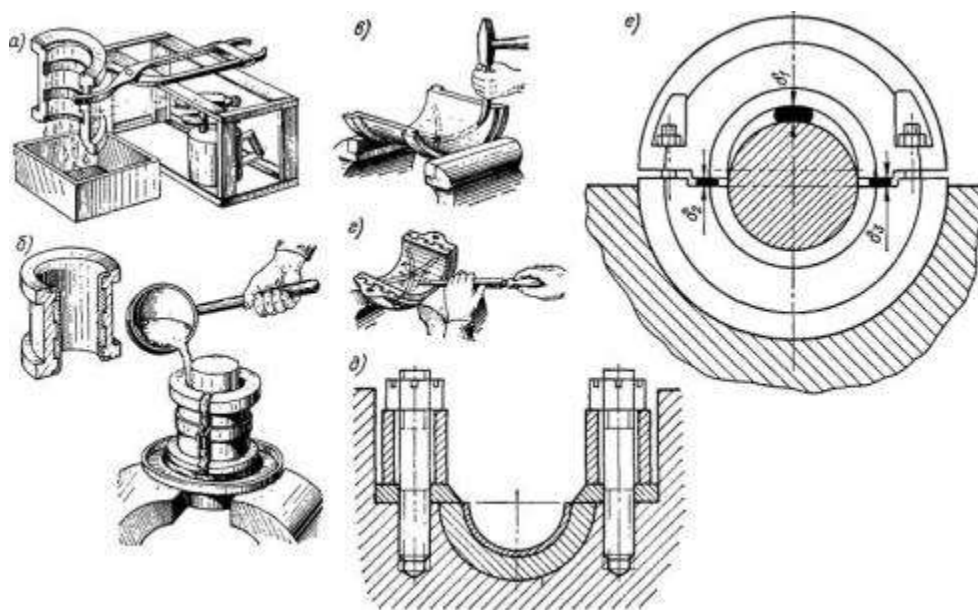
Ремонт разъемного подшипника скольжения: а — выплавка баббита; б -заливка баббита; в -вырубка смазочных канавок; г -шабрение; д — сборка; е- определение величины масляного зазора.
